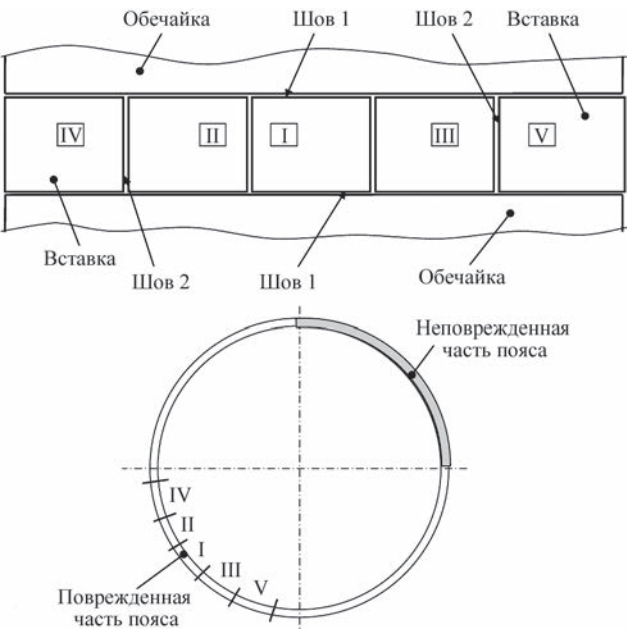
Очередность сварки вставок при ремонте регенератора Р-202
